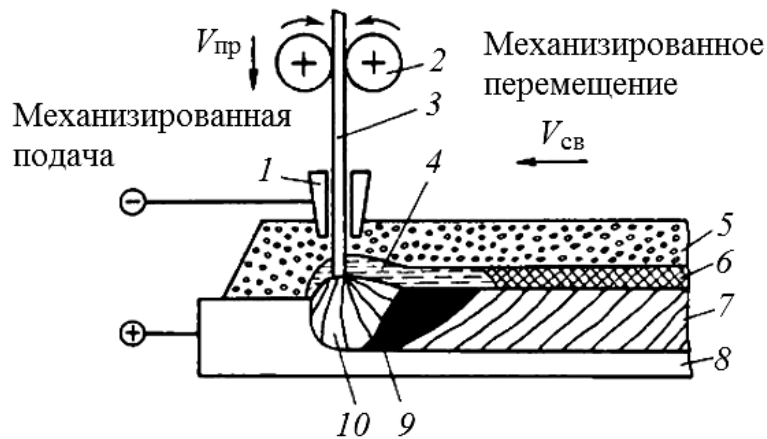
Схема автоматической дуговой сварки под флюсом
